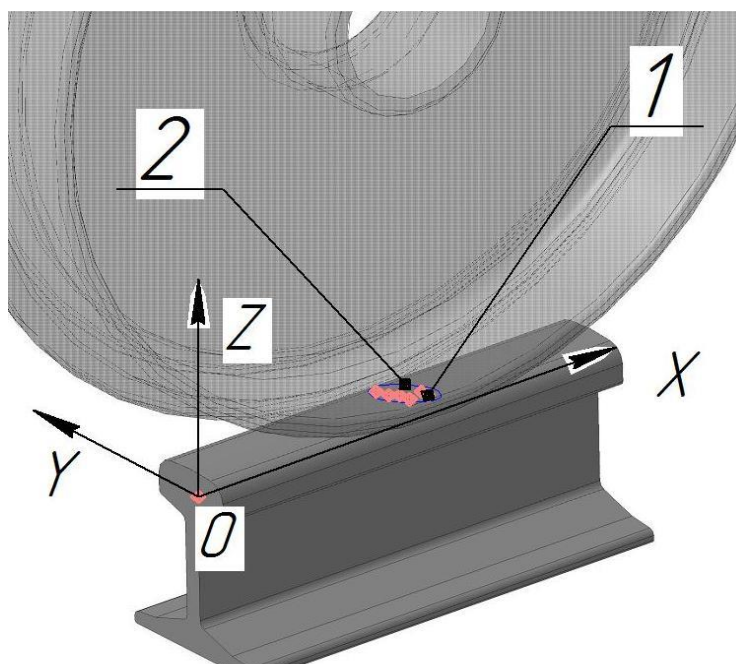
Опорна поверхня фрикційної пари колесо–рейка
